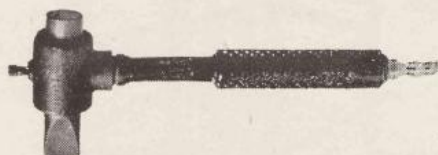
Fer à souder, à chauffage continu, non soufflé.
